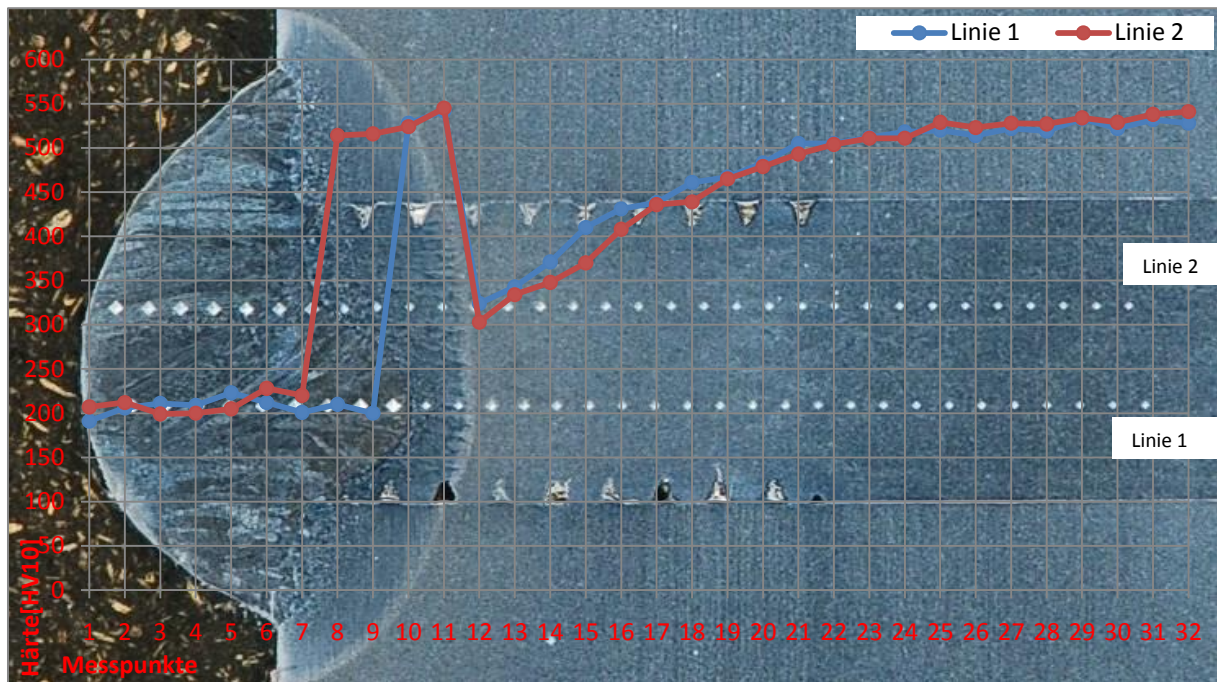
Härteverlauf bei der Implant-Probe 15; SG, WEZ, GW
